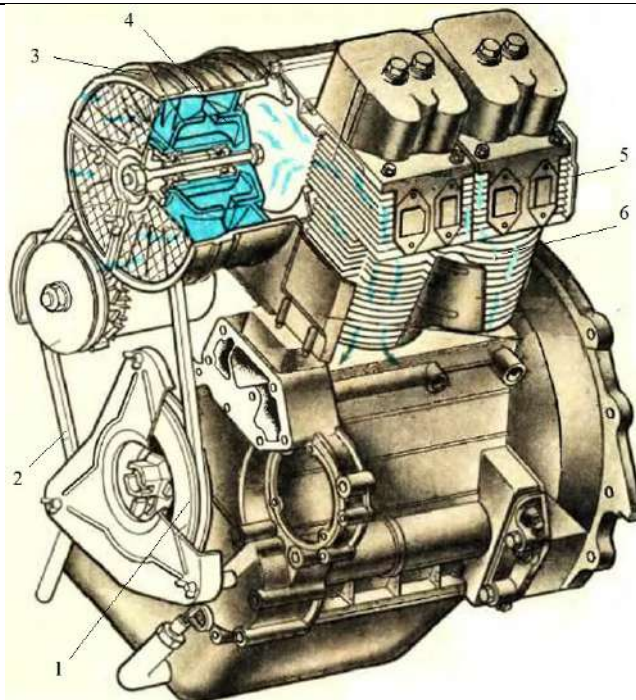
Автомобильный двигатель с принудительной воздушной системой охлаждения: 1 – шкив коленвала; 2 – ремень привода вентилятора; 3 – вентилятор принудительного охлаждения; 4 – направляющее устройство; 5 – головка цилиндра с рёбрами охлаждения; 6 – цилиндр с рёбрами охлаждения
